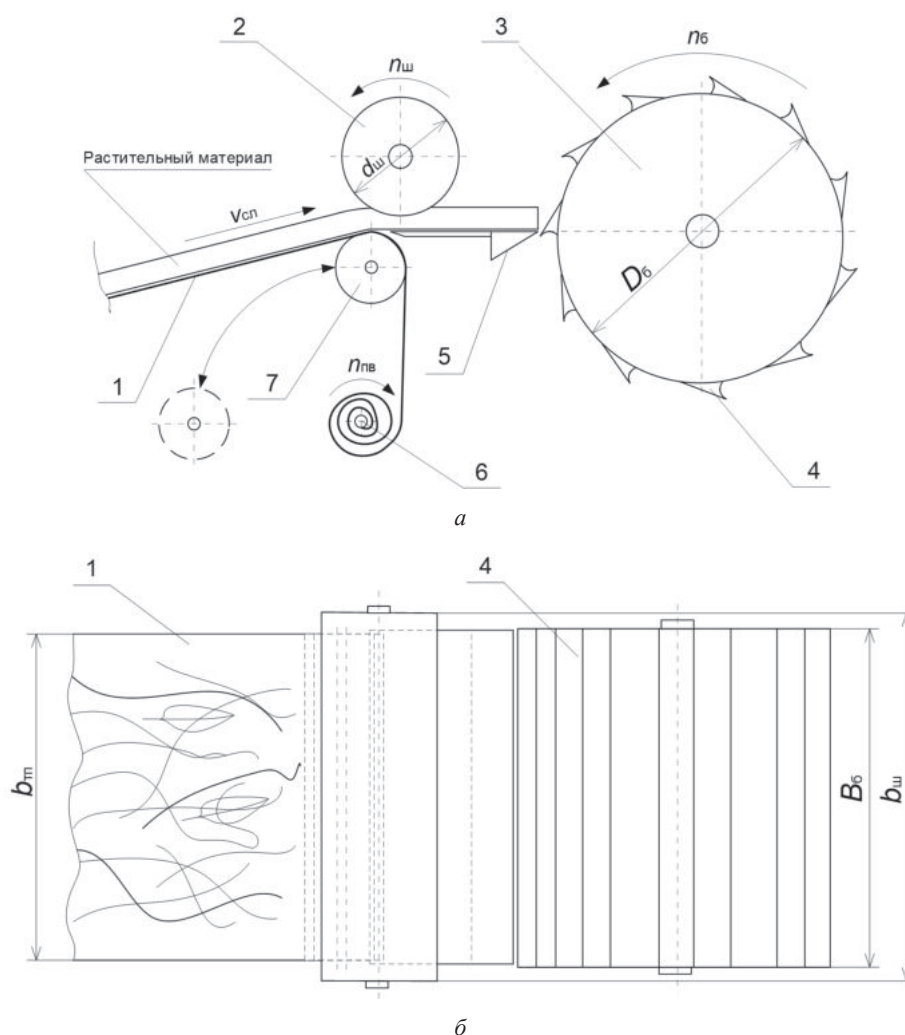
Конструктивно-технологическая схема устройства для подбора и измельчения органических отходов тепличного производства: *а* – вид сбоку; *б* – вид сверху; 1 – транспортировочное полотно; 2 – шнек со встречной навивкой; 3 – ножевой барабан; 4 – нож; 5 – противорежущая пластина; 6 – подающий валец; 7 – прижимной валец
